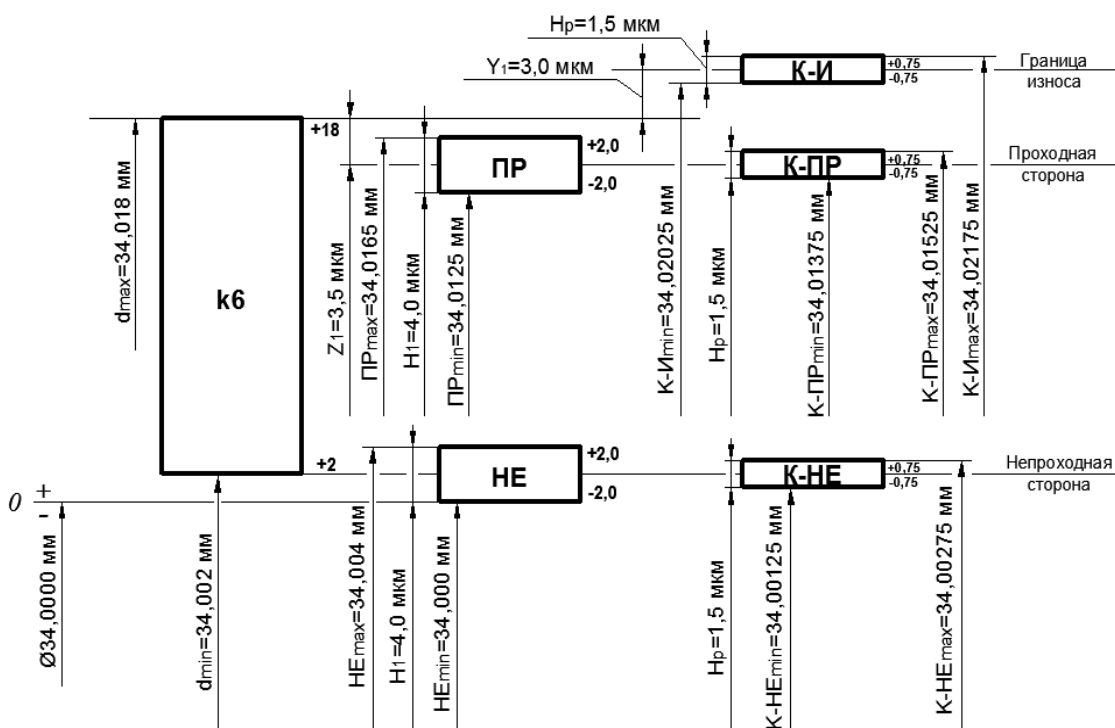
Схема расположения полей допусков калибров для контроля вала $\varnothing 34k6$ и контрольных калибров
